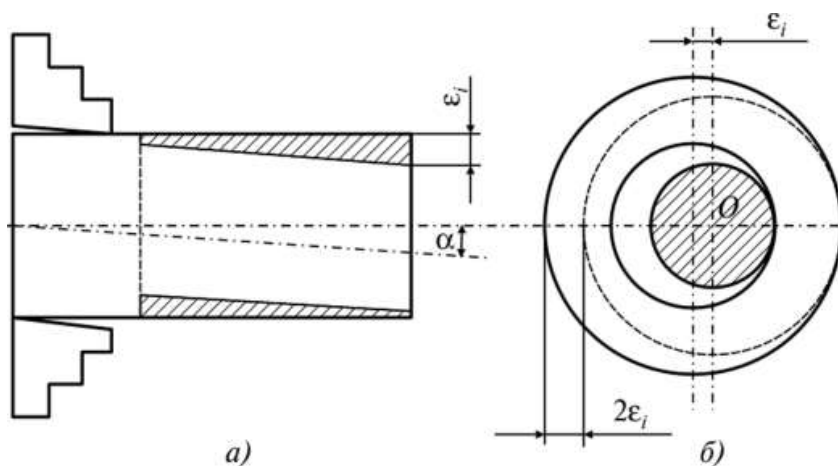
Вплив похибки установки на величину припуску: *a* — обробка валика в патроні; *б* - обробка втулки по зовнішній поверхні з базуванням на оправці із зазором.
